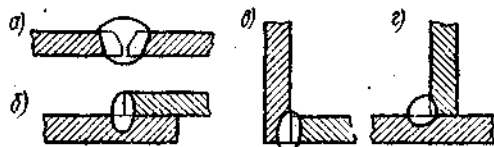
Типы сварных соединений: а - стыковое; б - нахлесточное; в - угловое; г - тавровое
